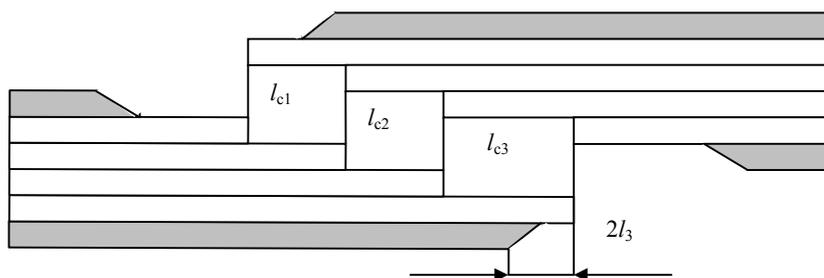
Схема ступенчатой разделки стыка многослойной РТКЛ
